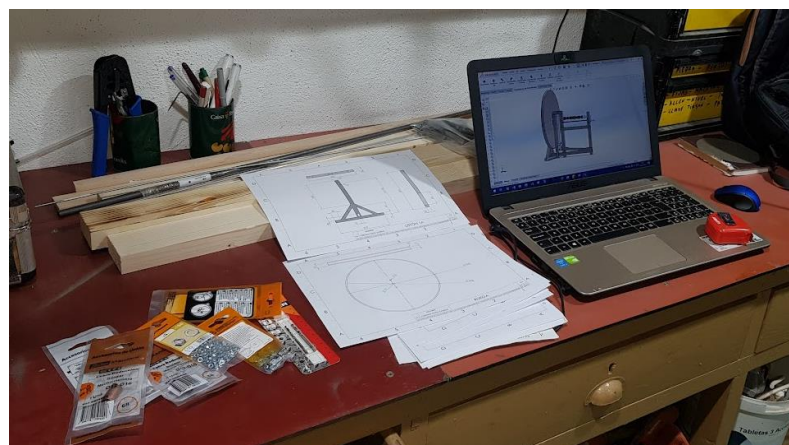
Planos y preparación del montaje. Fuente: Elaboración propia
